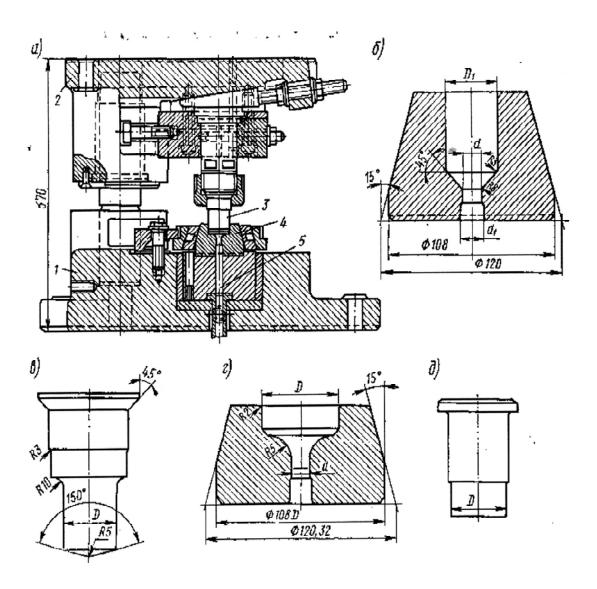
Схема двухручьевого штампа и формообразующего инструмента для выдавливания мелких поковок (типа клапанов):
